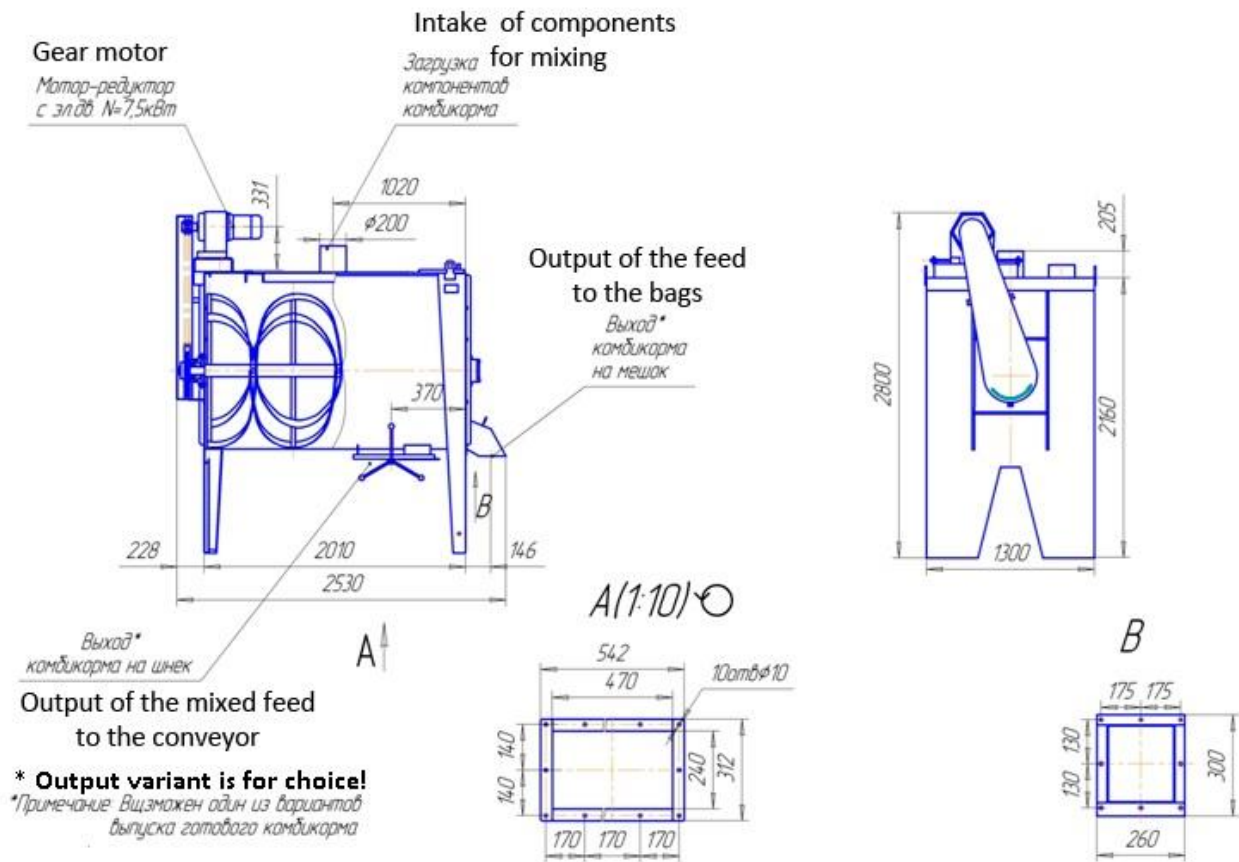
Габаритные, установочные и присоединительные размеры смесителя P1-БСК.
